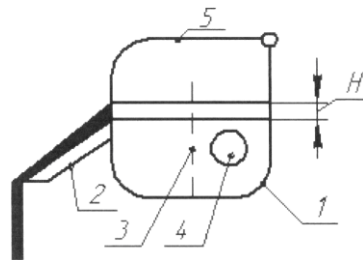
Наливна головка із зливною греблею: 1 - головка; 2 - зливна гребля; 3 - сітка для видалення бульбашок; 4 - труба для подавання лаку; 5 - кришка
